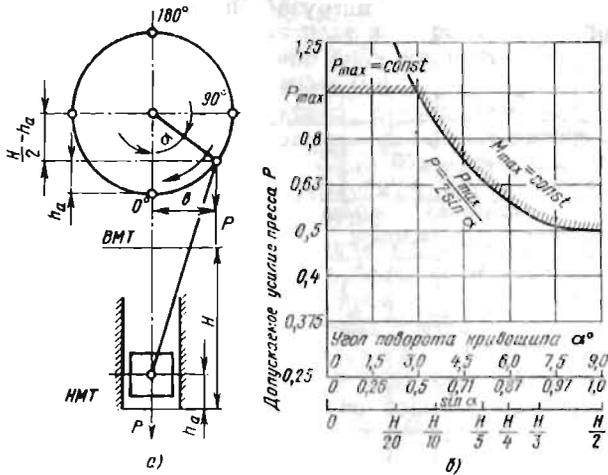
Допускаемое усилие кривошипного пресса:
